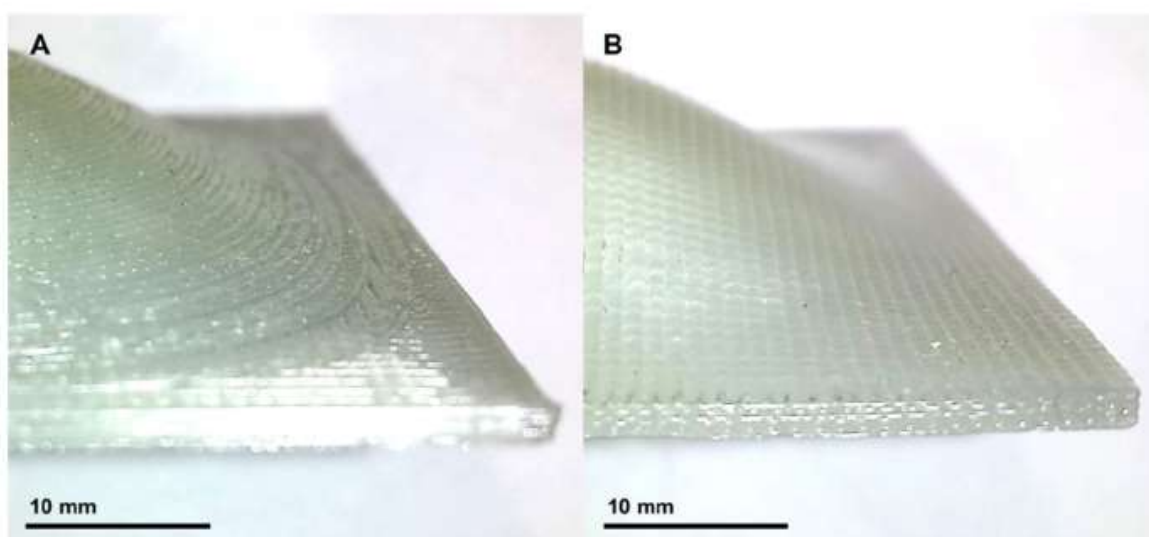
Totožný povrch vytvořen konvenčním slicingem [8].
